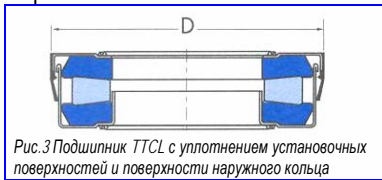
Подшипник TTCL с уплотнением установочных поверхностей и поверхности наружного кольца
